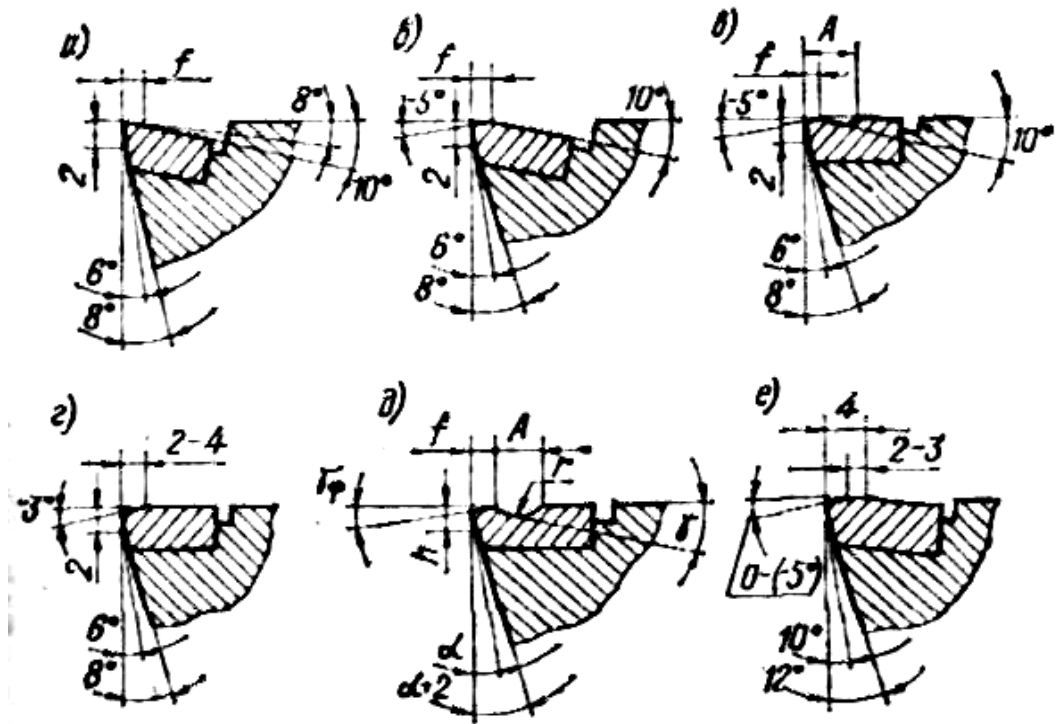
Форми заточування різців з пластинами із твердого сплаву.
